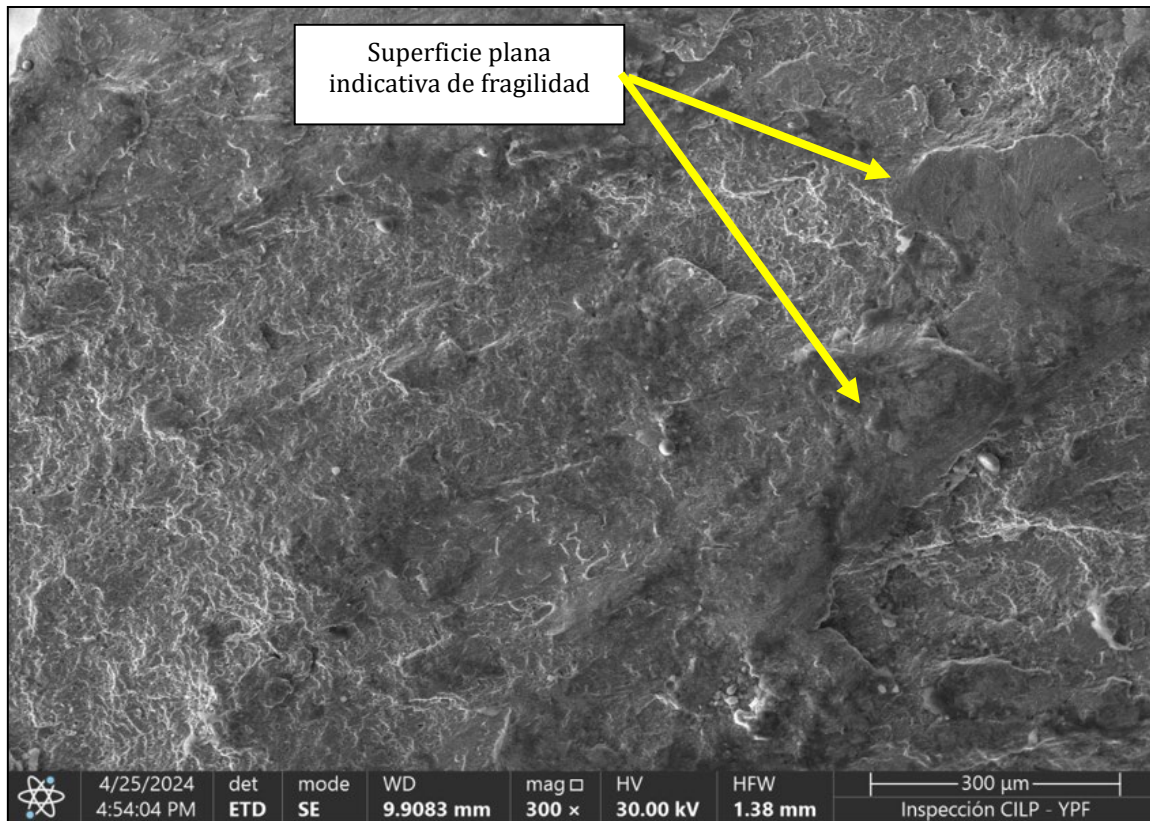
Superficie de fractura – Codo superior – Cordón circunferencial. Se observó a lo largo de todo el espesor de la soldadura este tipo de fractura.
